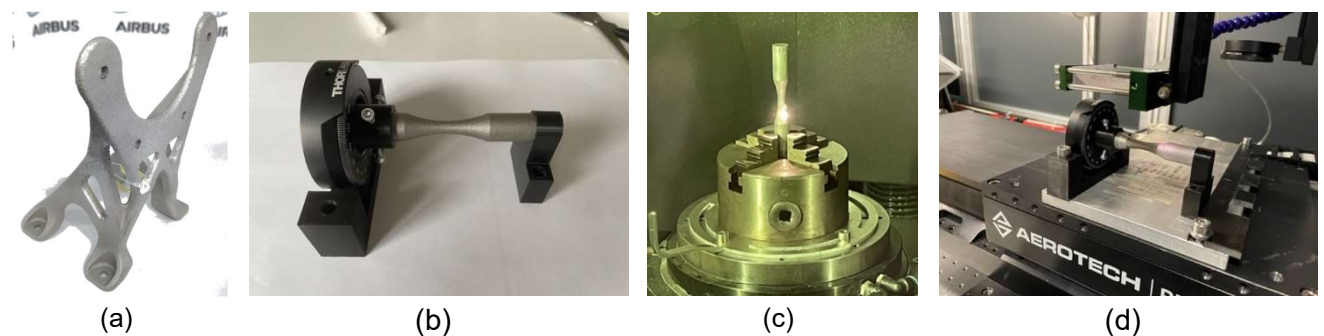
(a) 3D-Bauteilgeometrie als Demonstrator (b) Exemplarische Rundproben für Ermüdungsuntersuchungen die mittels DLW (c) und DLIP (d) bearbeitet wurden.
